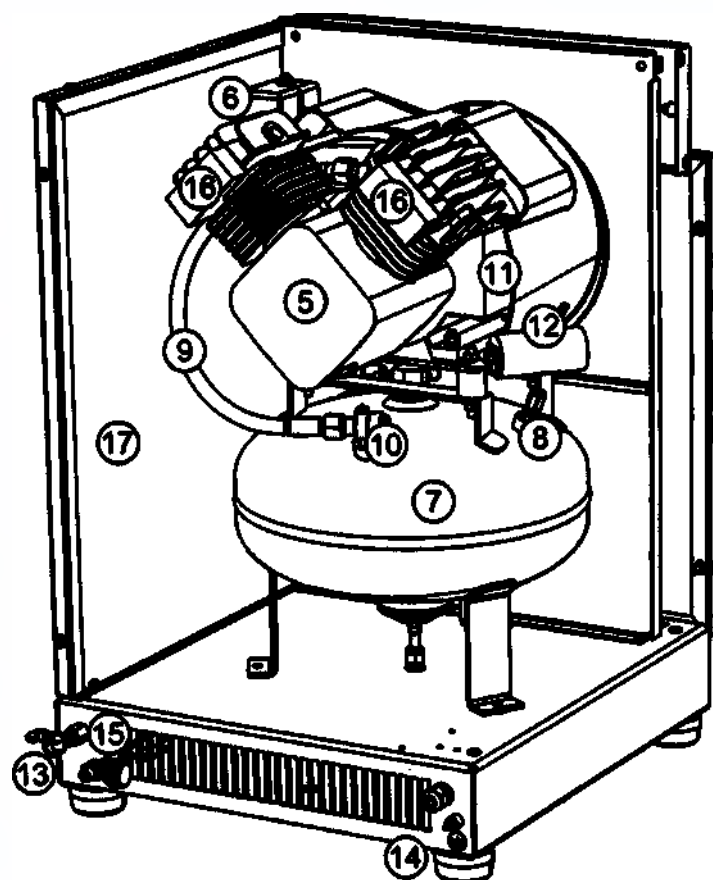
Общий вид компрессора KM-16.VS204K
